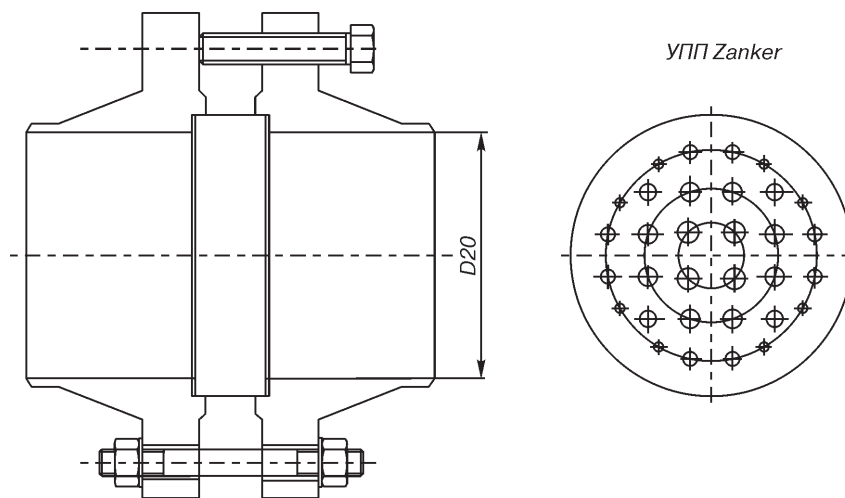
Схема дискового устройства подготовки потока Zanker.
